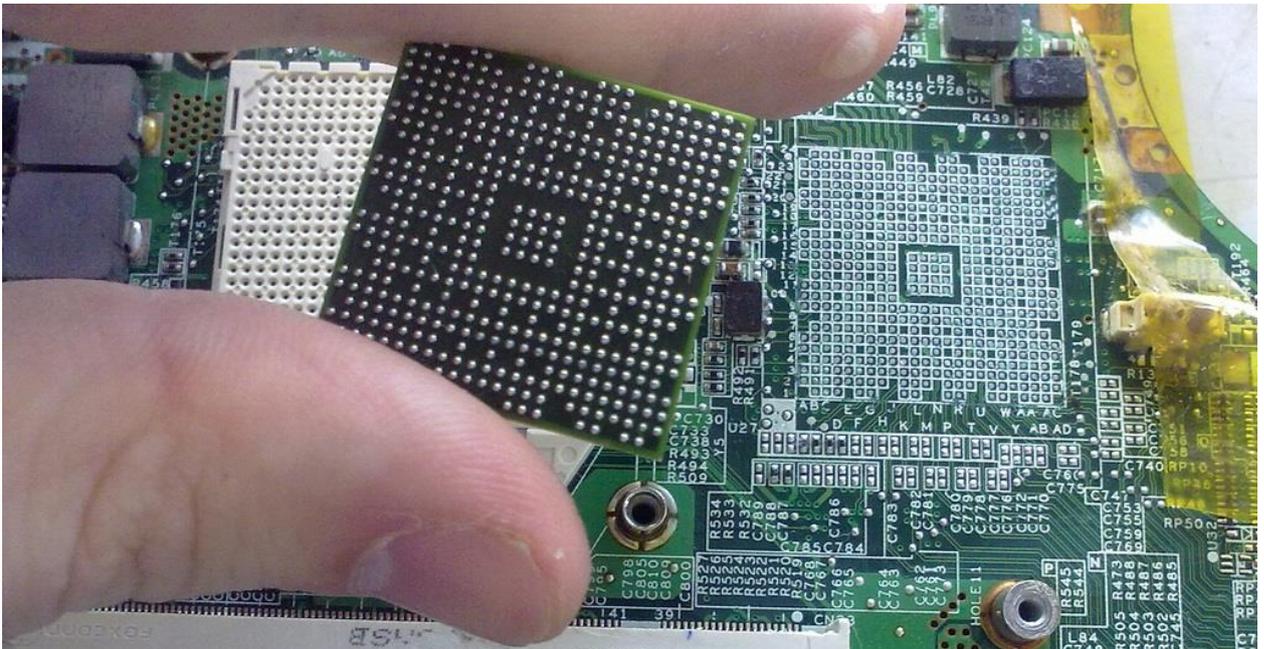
Монтаж корпуса с выводами типа BGA
